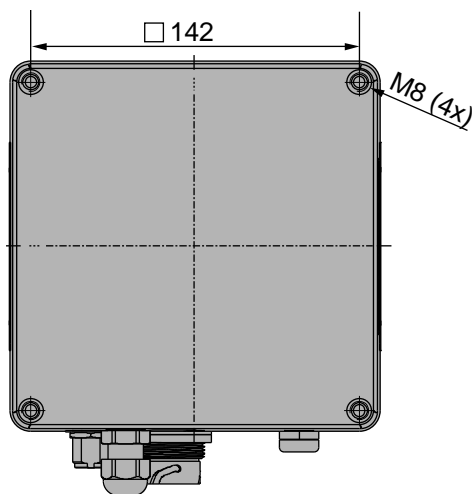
BNK6500 Rückseite - Befestigung im Schaltschrank
